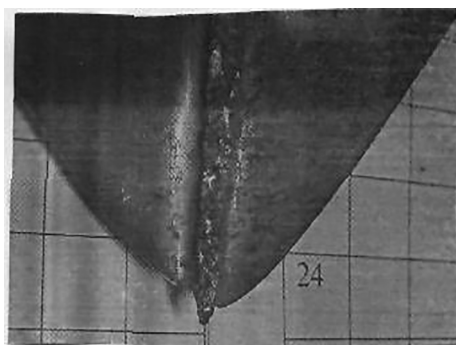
Характерный износ двух материалов (65Г (1) и 50ХГА (2)) при соединении их с одной стороны сварочным швом, а с другой – наплавкой (механическая смесь марки ПС-14-60)
